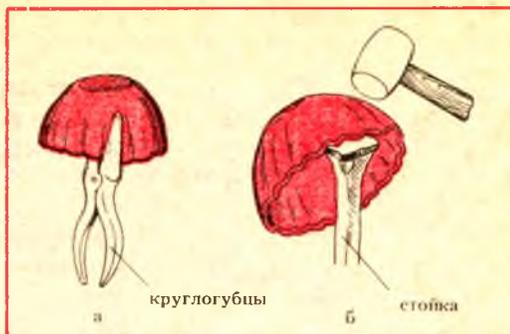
Оформление сферы: а — изготовление гофр; б — осадка гофр
